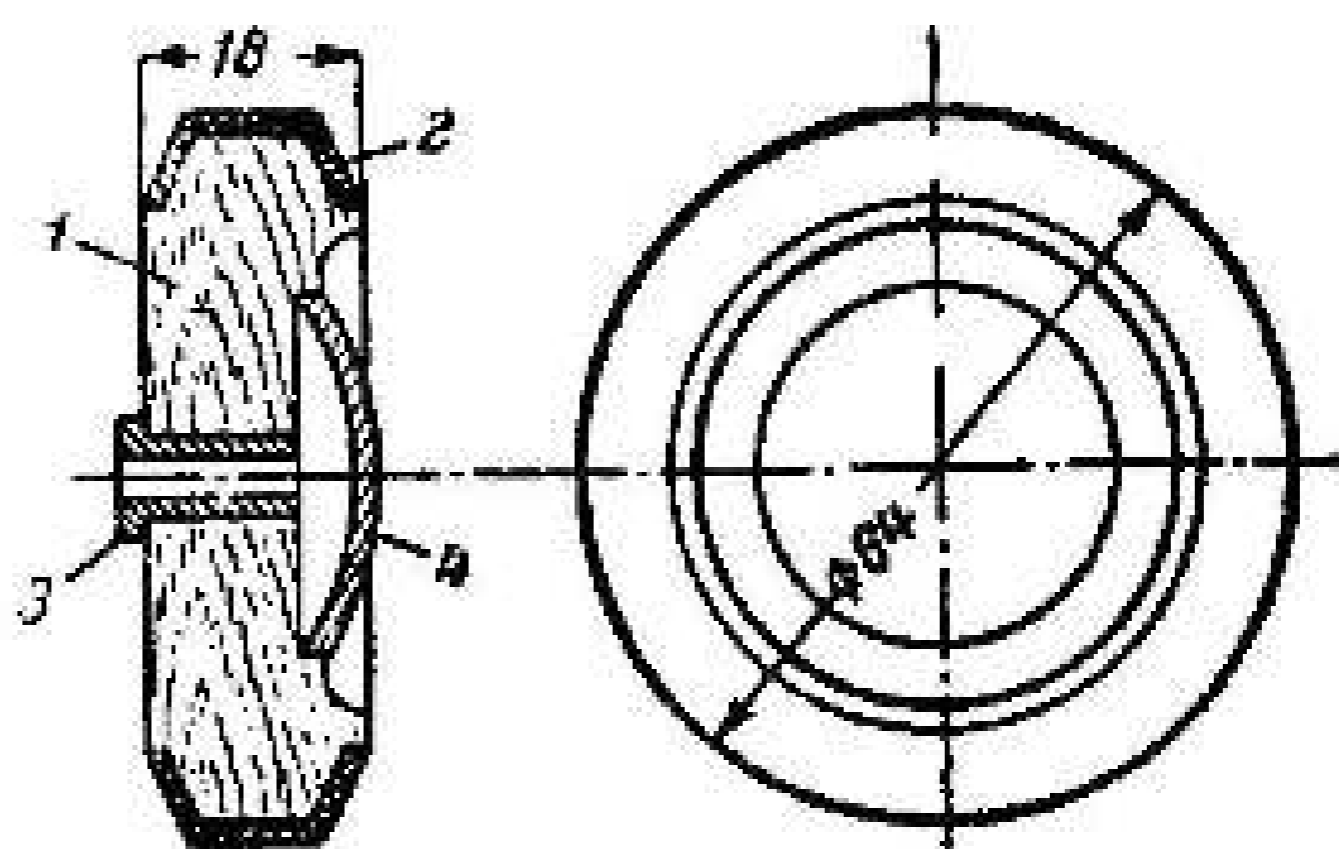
Колесо автомодели, изготовленное на токарном станке:
